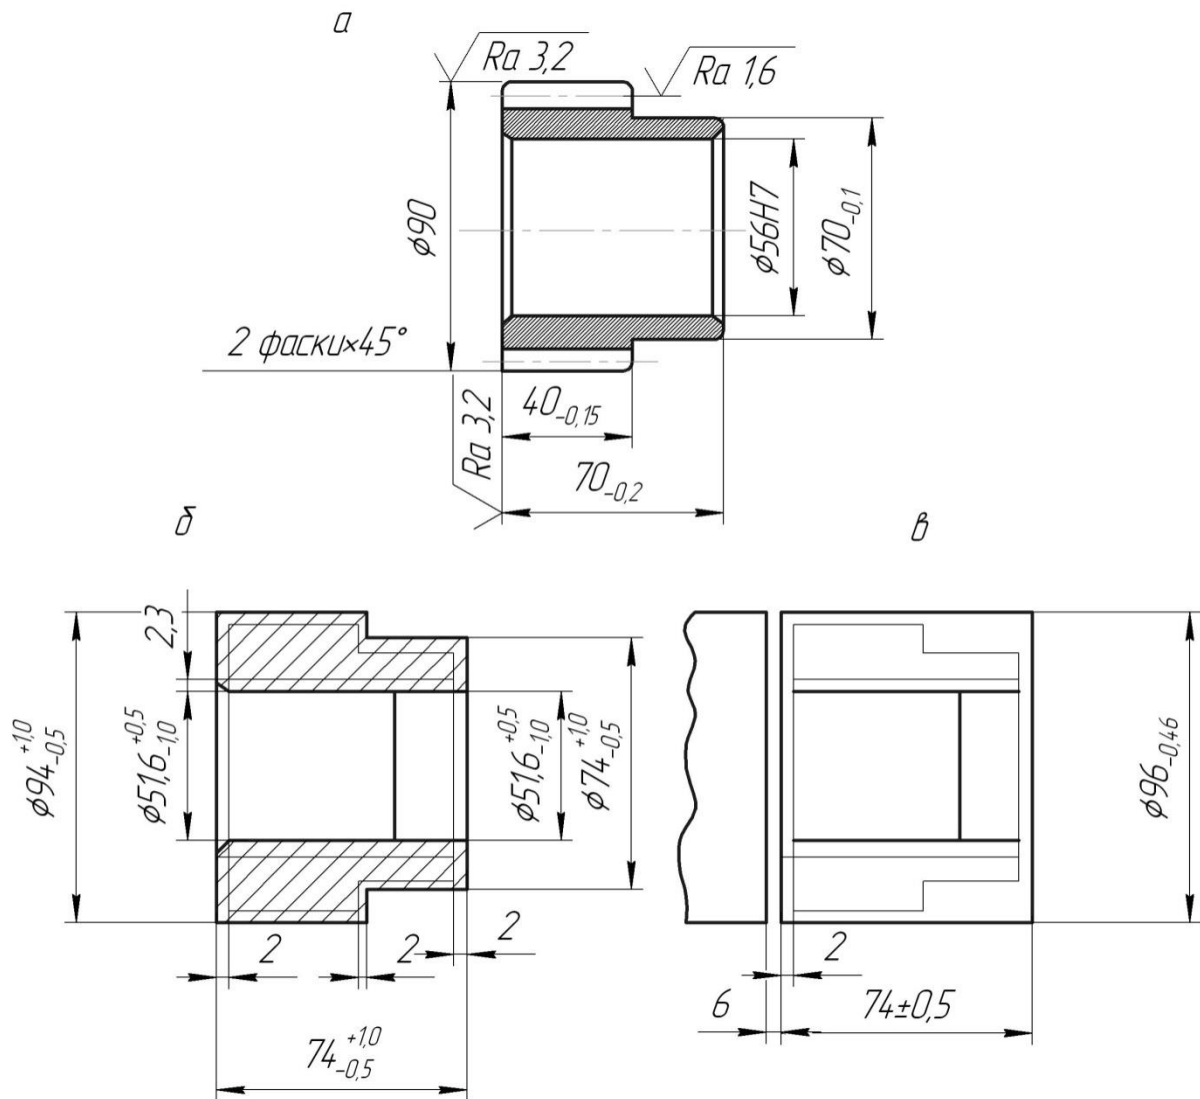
Эскизы чертежей детали и заготовки: а - детали; б - штампованной заготовки; в – заготовки из проката
